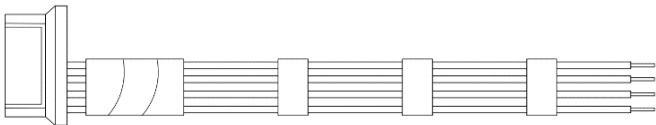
Внешний вид соединителя MPCB.468349.028
